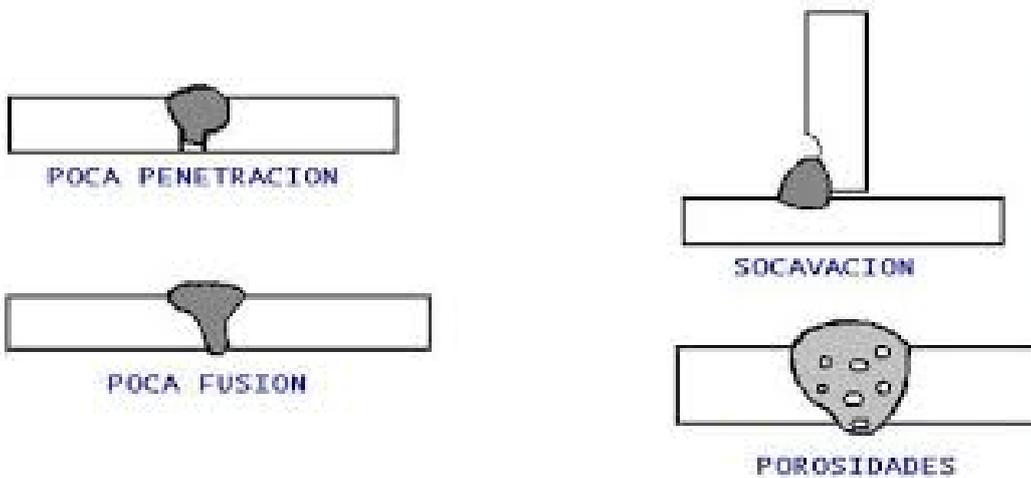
Defectos y fallas por soldadura.
